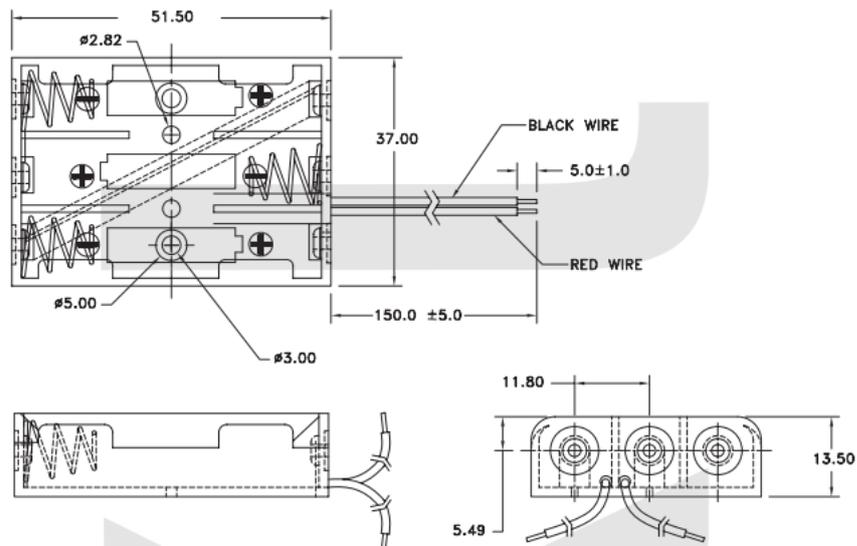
Размеры батарейного отсека на 3 батарейки формата ААА
